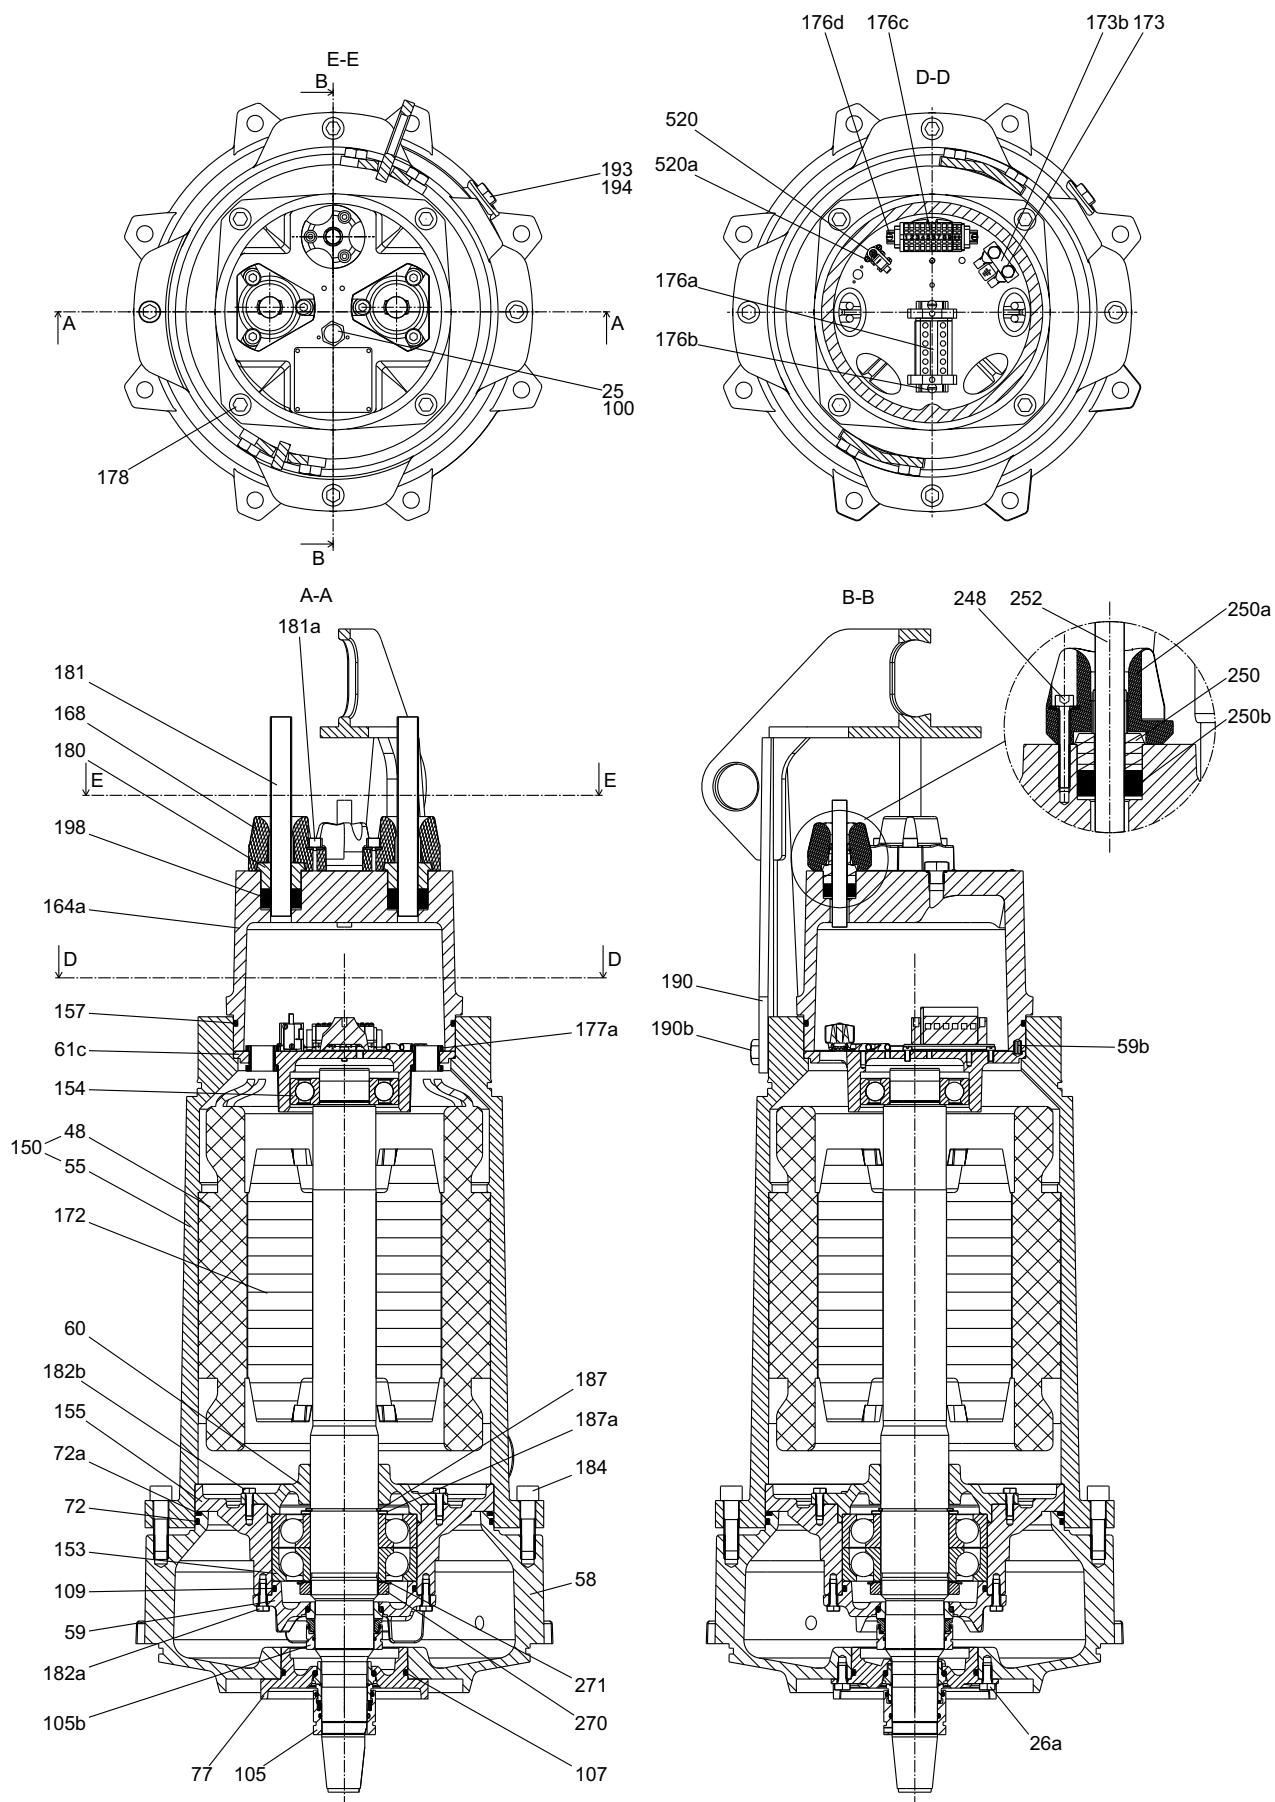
Стандартный электродвигатель с охлаждающим кожухом
